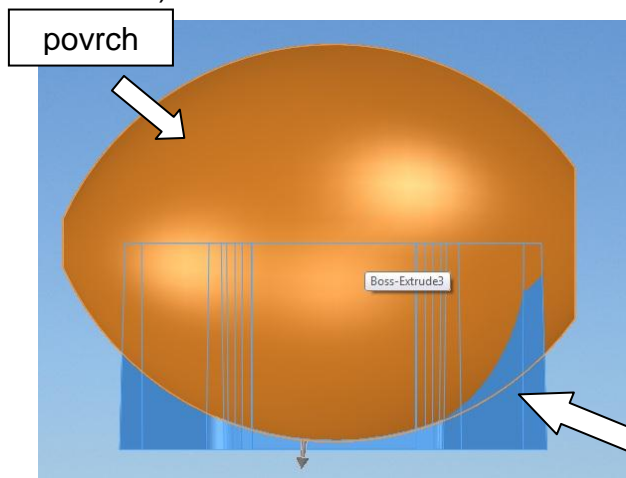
Odsazení skici o 5 mm od povrchu těla směrem dovnitř
